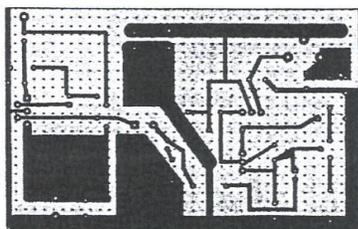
PLACA DE FIXAÇÃO IMPRESSA DO MODULADOR
